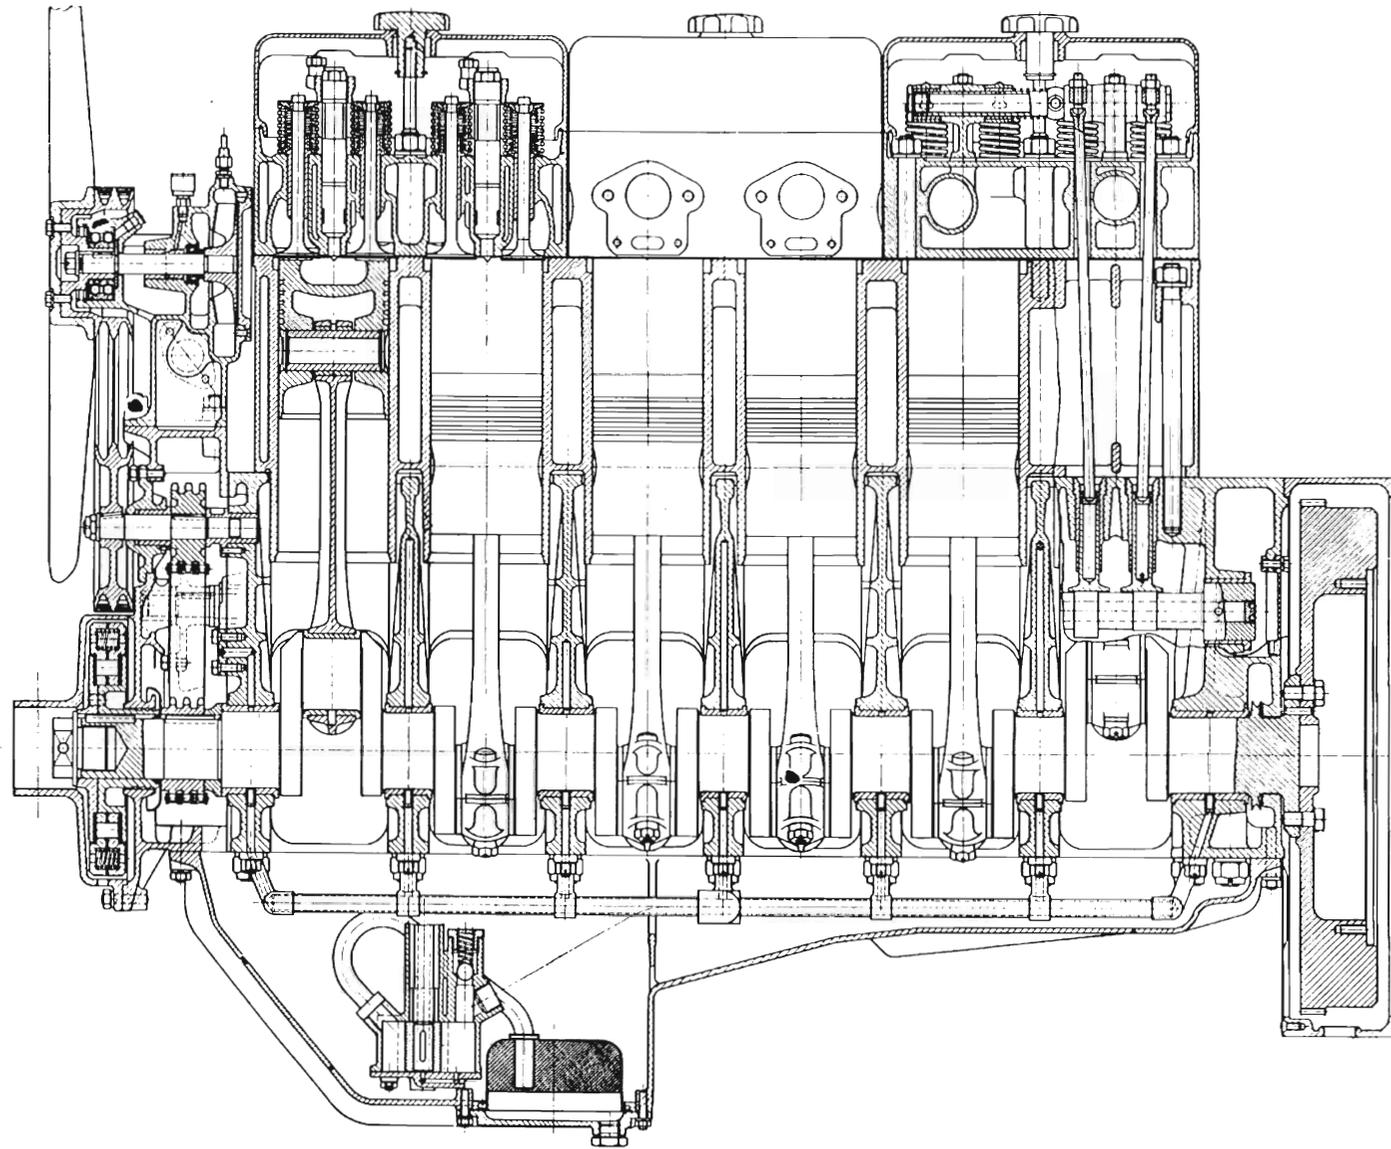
Längsschnitt durch den 6-Zylinder-Motor
